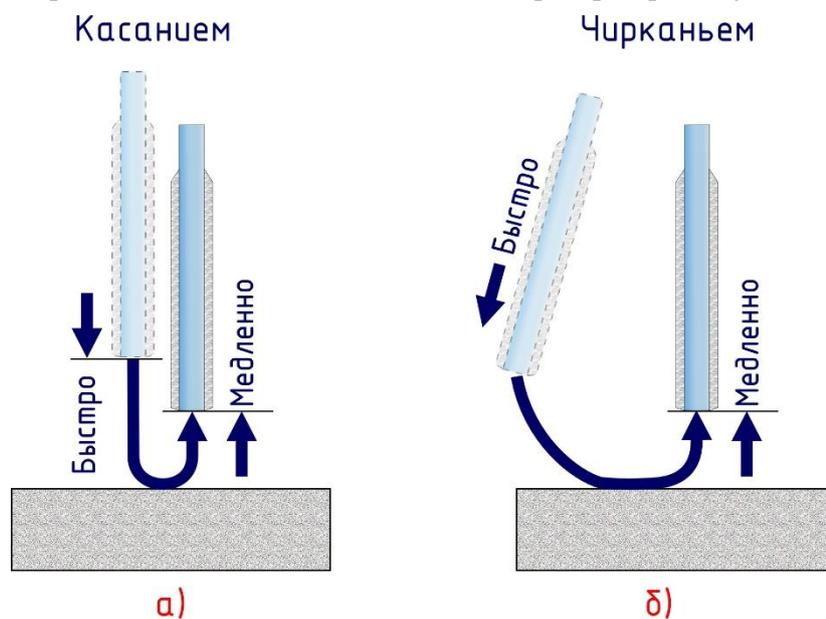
Способы зажигания сварочной дуги плавящимся покрытым электродом
